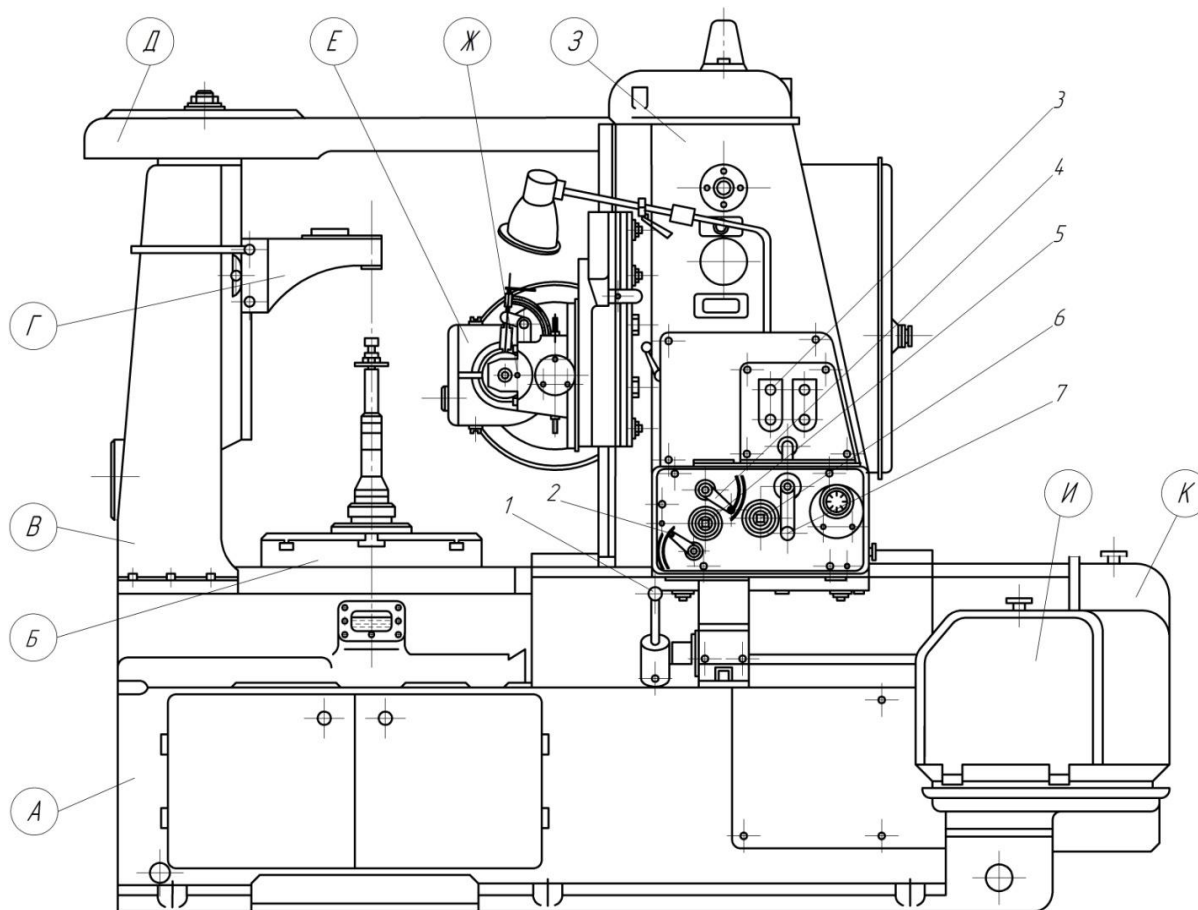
Общий вид зубофрезерного полуавтомата модели 5Д32. Основные узлы станка:
